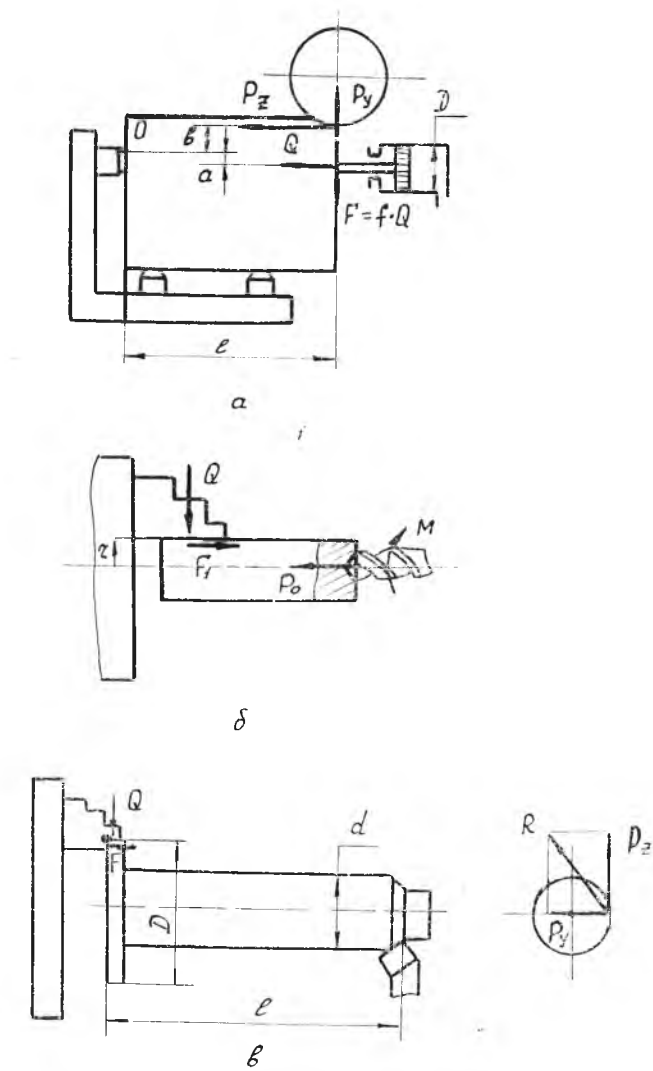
Расчетные схемы к определению величины зажимного усилия, удерживающего заготовку: а — при фрезеровании; б — при сверлении на токарном станке; в — при точении на токарном станке
